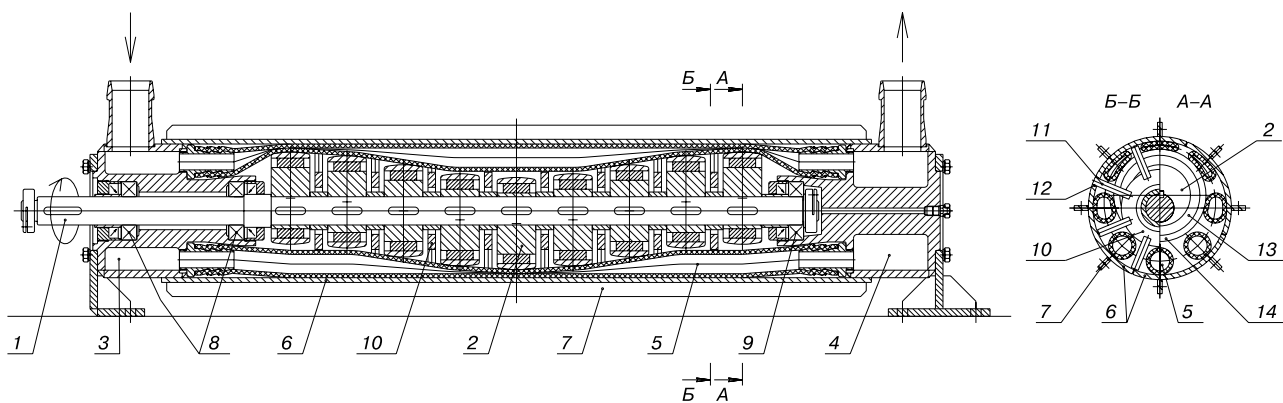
Насос «Помпж-1» (привод не показан): 1 – вал; 2 – эксцентрик; 3 – коллектор впускной; 4 – коллектор выпускной; 5 – рукав резиновый; 6 – крышка; 7 – ребро; 8, 9 – опоры подшипниковые; 10 – звездочка; 11 – спица; 12 – паз; 13 – подшипник (втулка); 14 – нажимное кольцо
